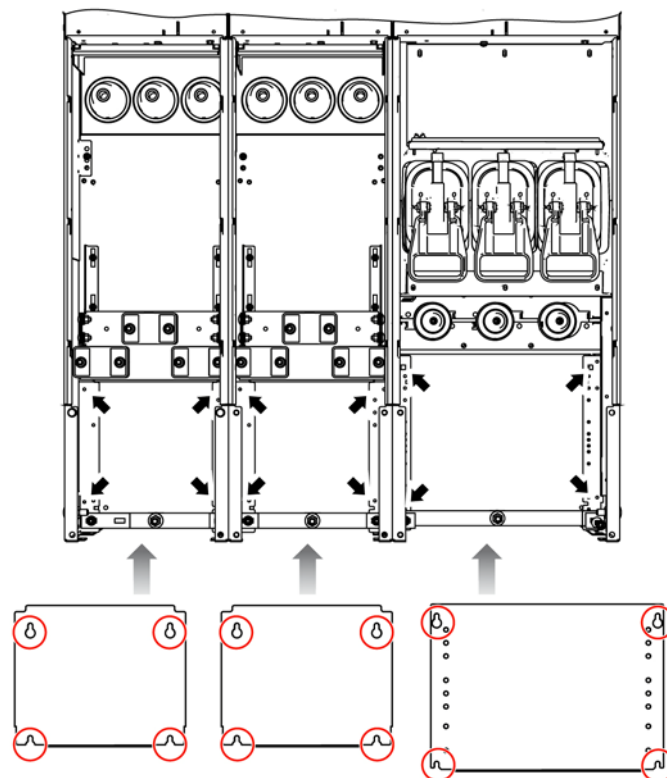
Монтаж нижней перегородки (вид спереди)
